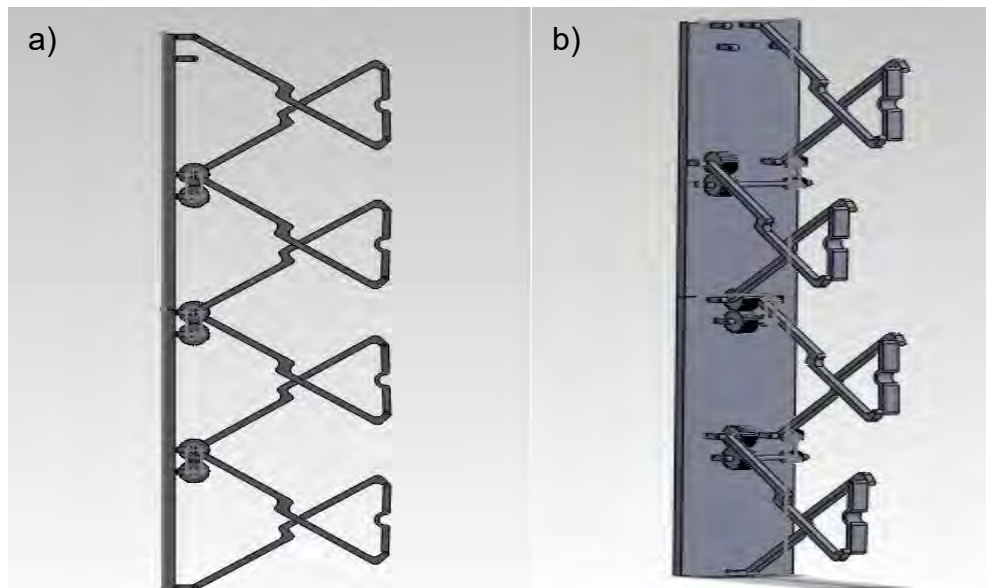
Conjunto de mecanismos de Chebyshev, a) vista frontal, b) vista en 3D
